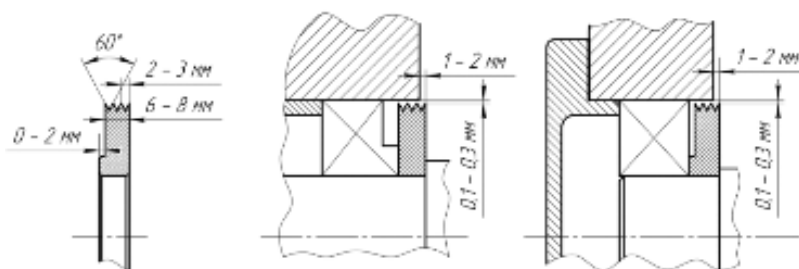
Конструкция мазеудерживающего кольца, подшипниковые узлы с использованием пластичного смазочного материала
